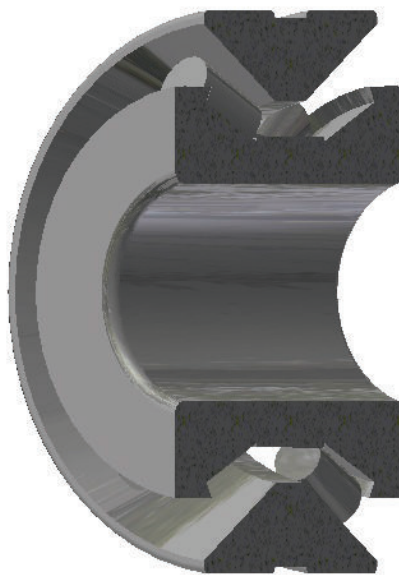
Corte transversal de rodamiento con contacto de rodadura autoalineante
